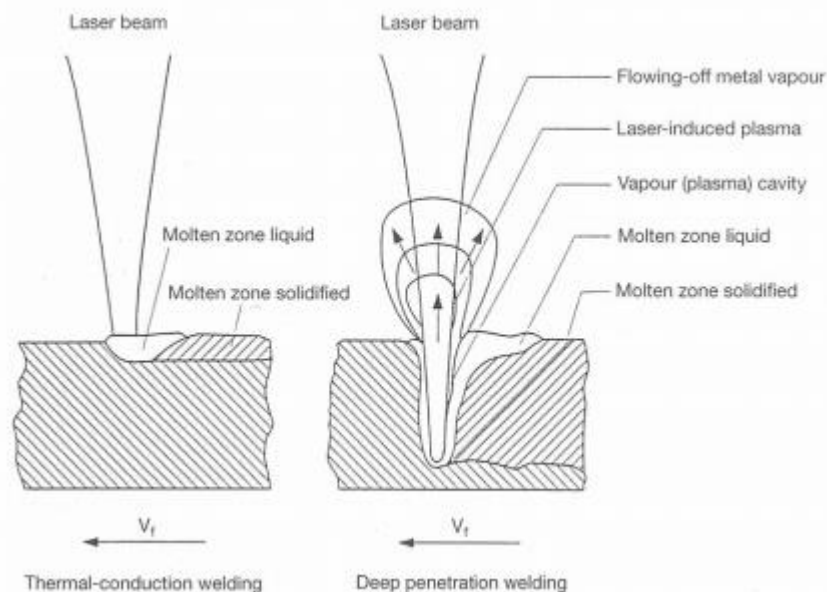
Representação esquemática do processo de soldadura laser, [2].
